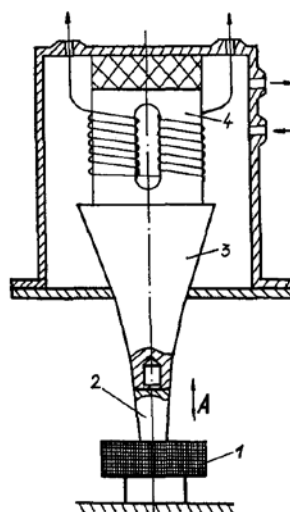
Принципиальная схема установки для ультразвуковой сварки
